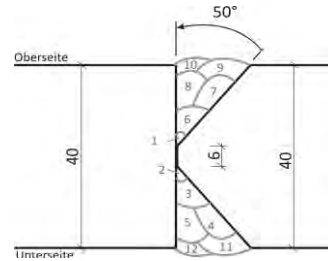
Schweißparameter der Probeschweißung Nr. 1
